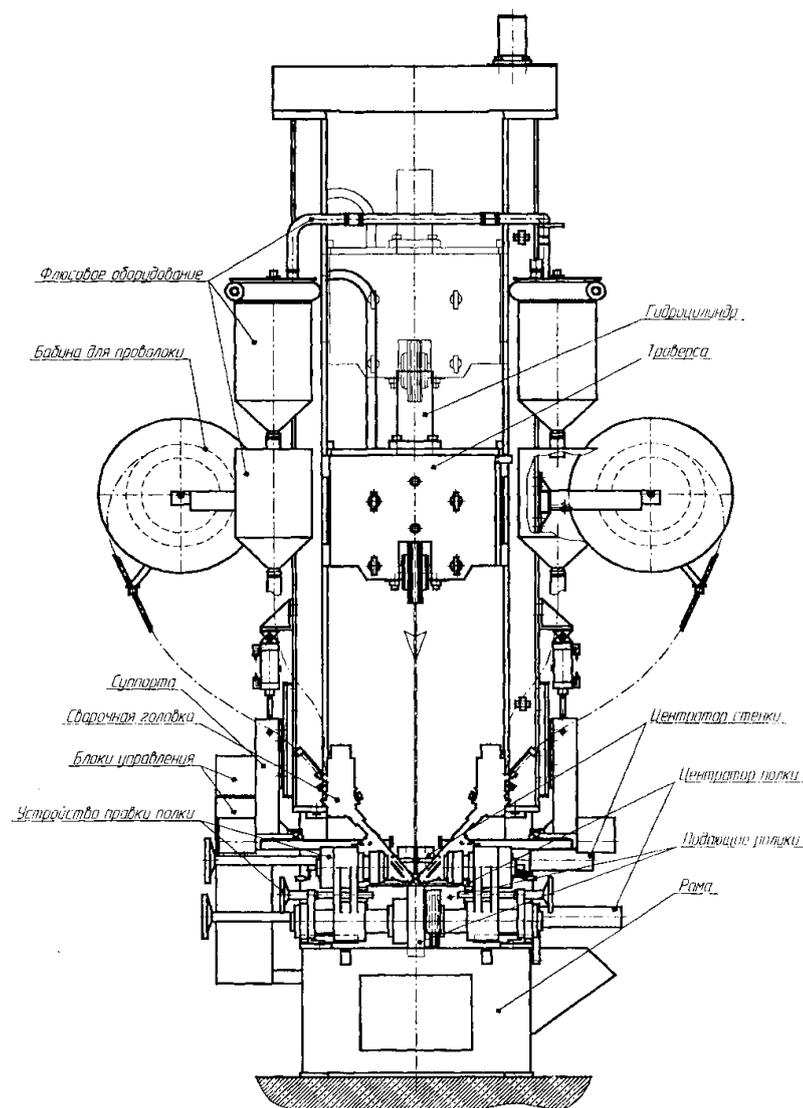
Установка для сварки балок ИТ 258 В А (фронтальная проекция)
